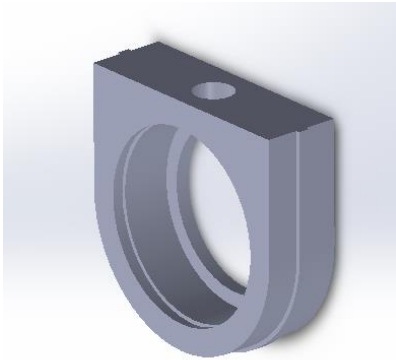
Carcasa Rodamiento guía. “Fuente: Autor”.
